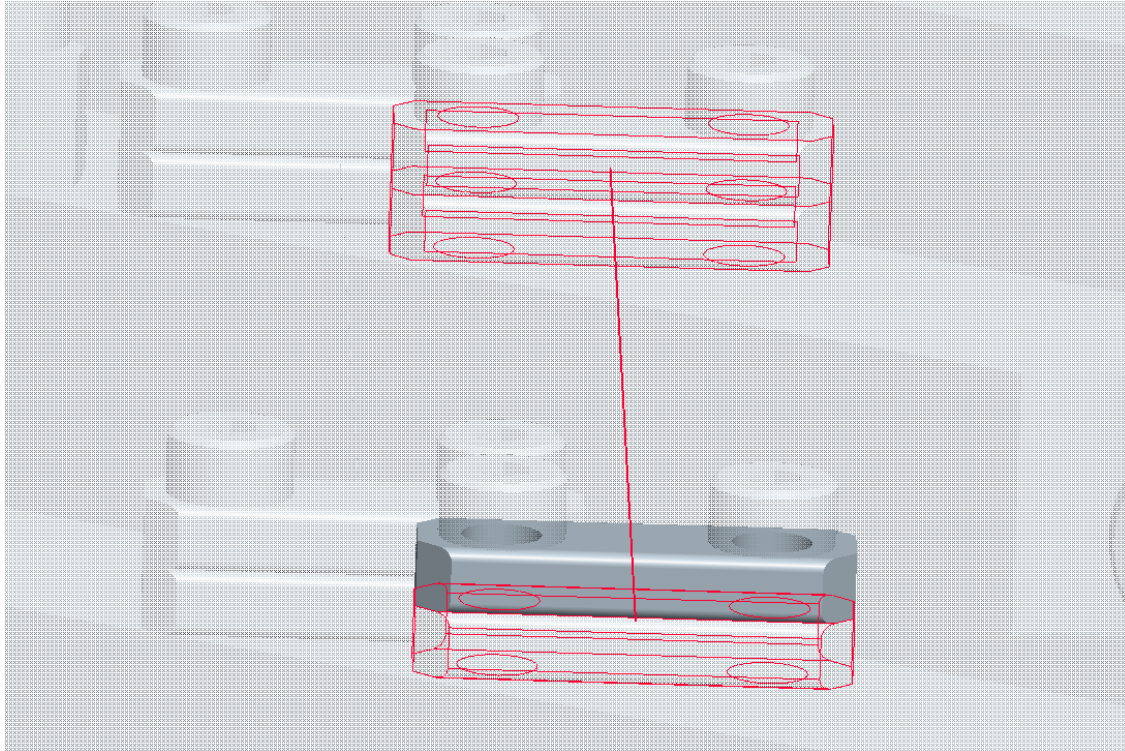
Faserklemme für eine Faser (Faser & Halterung rot hervorgehoben)
